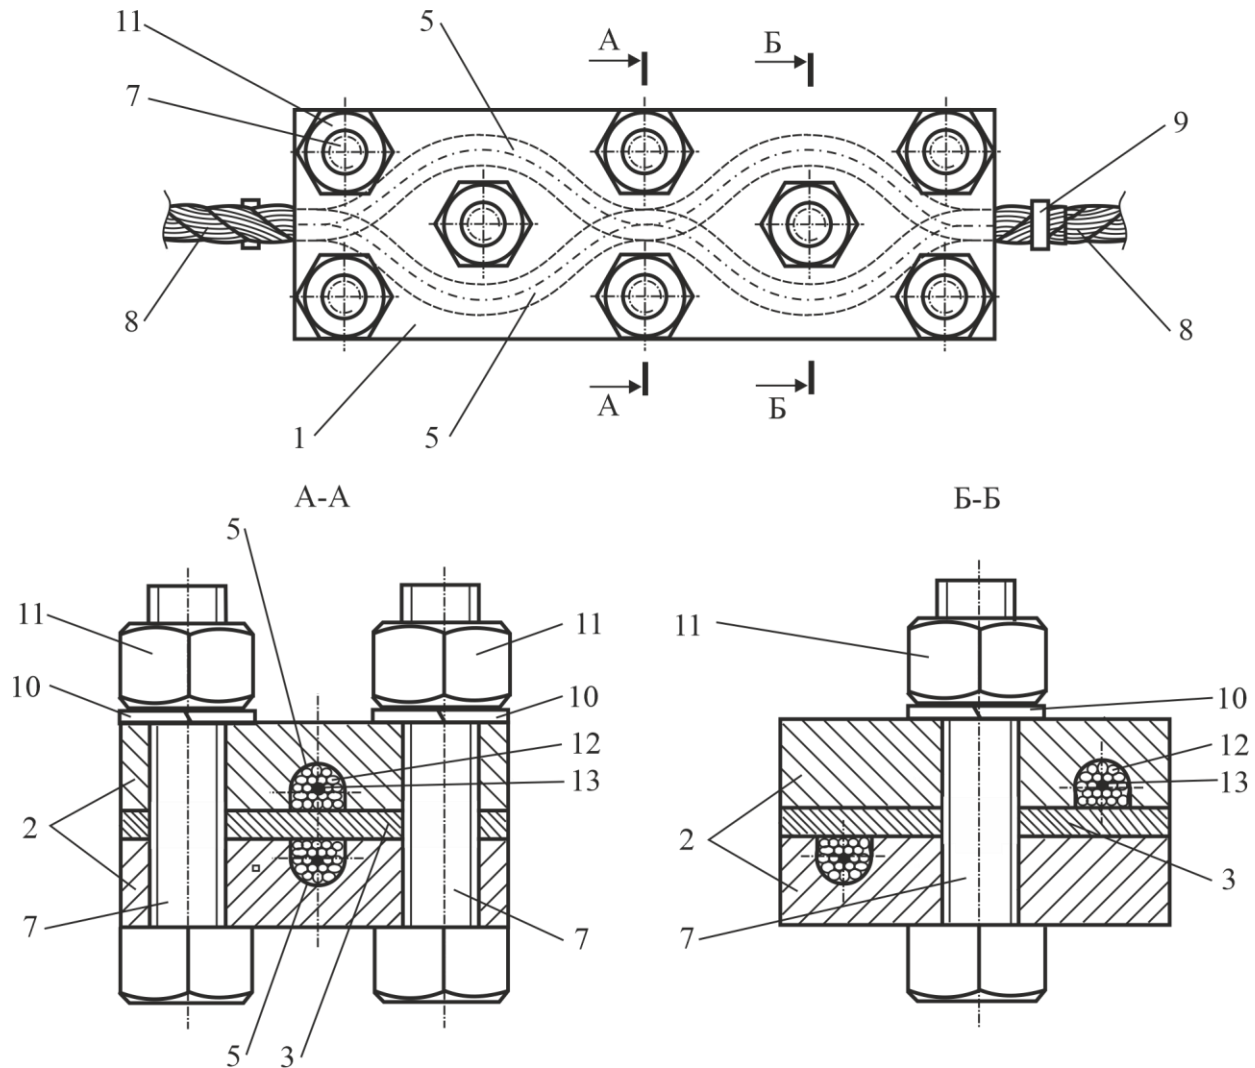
Конструкция быстроразъемного устройства для соединения концов канатов мобильных канатных дорог маятникового типа [8]: 1 - разъемный корпус; 2 - пластина корпуса; 3 - нажимная пластина; 4 - внутренняя поверхность; 5 – канавка; 6 - соосное отверстие; 7 - стяжной болт; 8 - соединяемый канат; 9 - предохранительная втулка; 10 - пружинная шайба; 11 – гайка; 12 - прядь каната; 13 - органический сердечник; 14 – рабочая поверхность нажимной пластины
